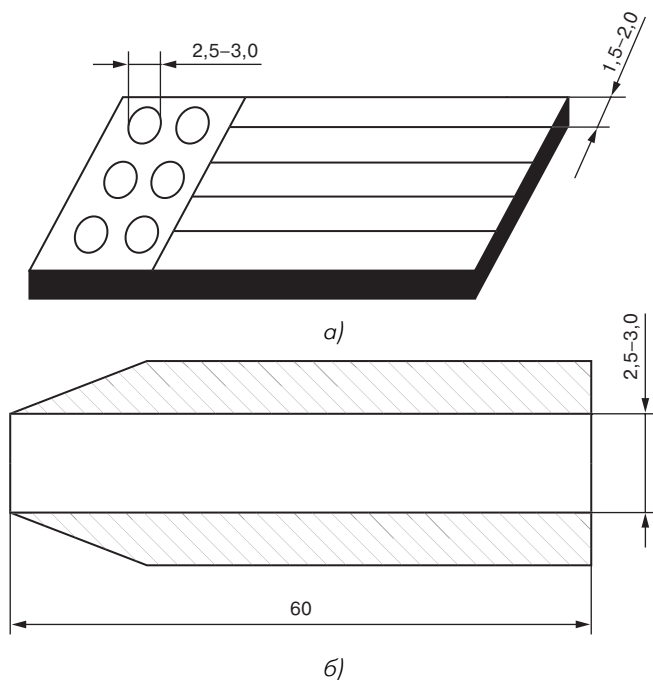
Заготовка кружков (а) и полосок (б) из изолянта
